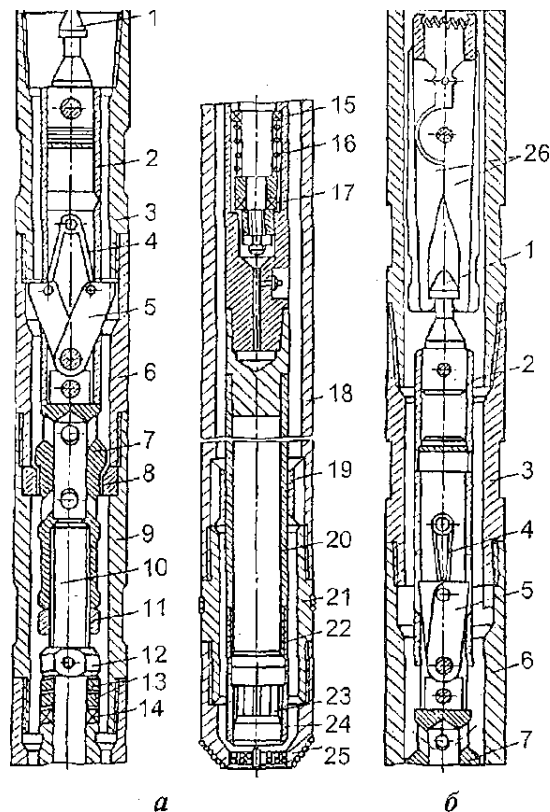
Двойной колонковый снаряд со съёмным керноприемником КССК-76 конструкции СКБ НПО "Геотехника": 1 - грибок; 2 - гильза; 3- переходник-центратор; 4 - пружина; 5 - защелка; 6 - переходник; 7 - корпус; 8 - опора; 9 - переходник; 10 - шпindelь; 11 - регулировочная гайка; 12 - зажимная гайка; 13 - резиновые манжеты; 14, 15 - упорные подшипники; 16 - пружина; 17 - упорный подшипник; 18 — колонковая труба; 19 - бронзовый центратор; 20 - керноприемная труба; 21 - расширитель; 22, 23- кернорвательное устройство; 24 - корпус кернорвателя; 25 - коронка; 26 - лапы ловителя.
